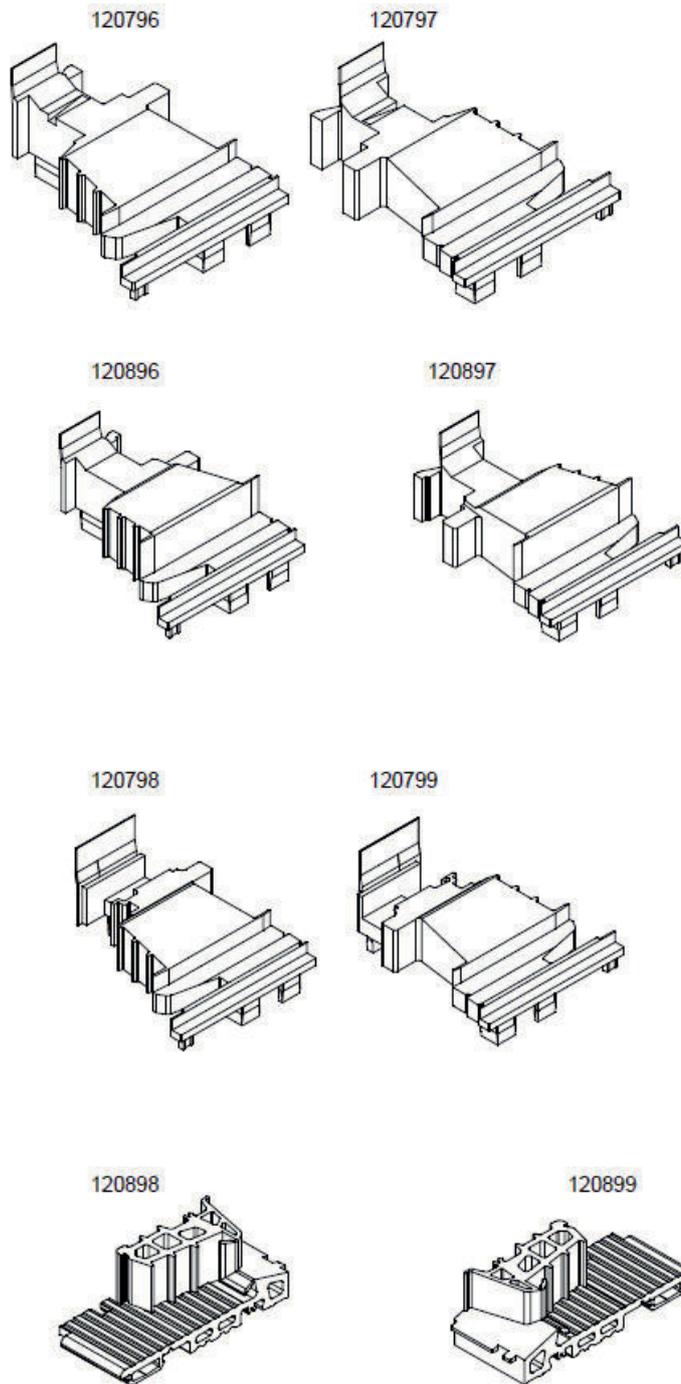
Elemente des beweglichen Pfostens und Eckdichtungen
